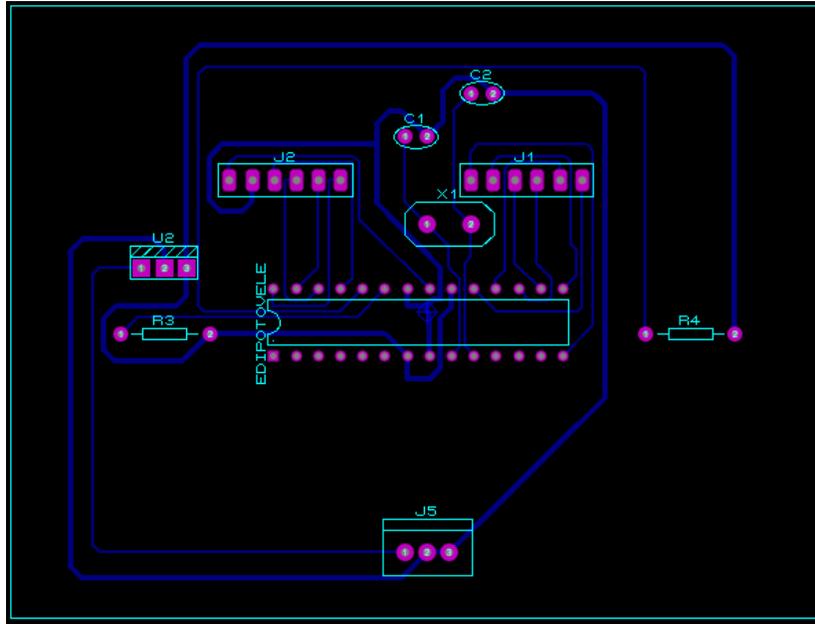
PCB layout do Módulo de Controle de Velocidade<sup>27</sup>
